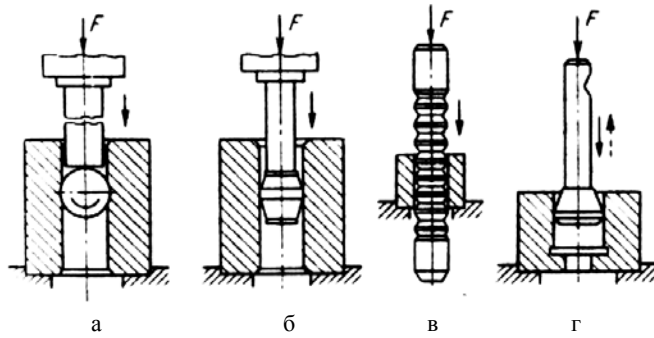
Схеми обробки отворів деталей інструменту поверхневою пластичною обробкою ковзанням: а – кулькою; б – бочкоподібною прошивкою; в – складовою багатоеlementною прошивкою; г – прошивкою-оправкою для глухих отворів
